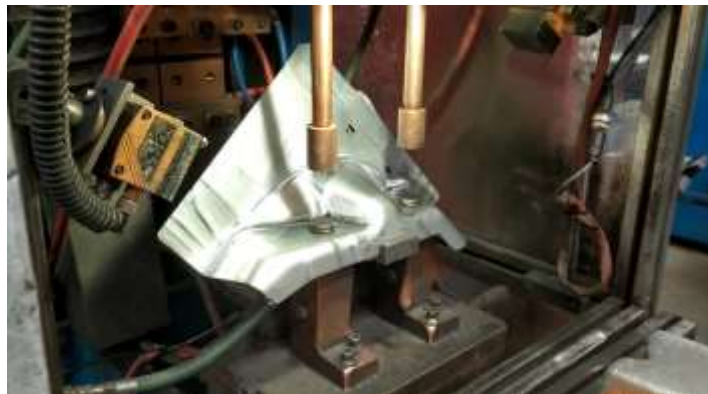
Exemplo de máquina de soldadura pedestal.
